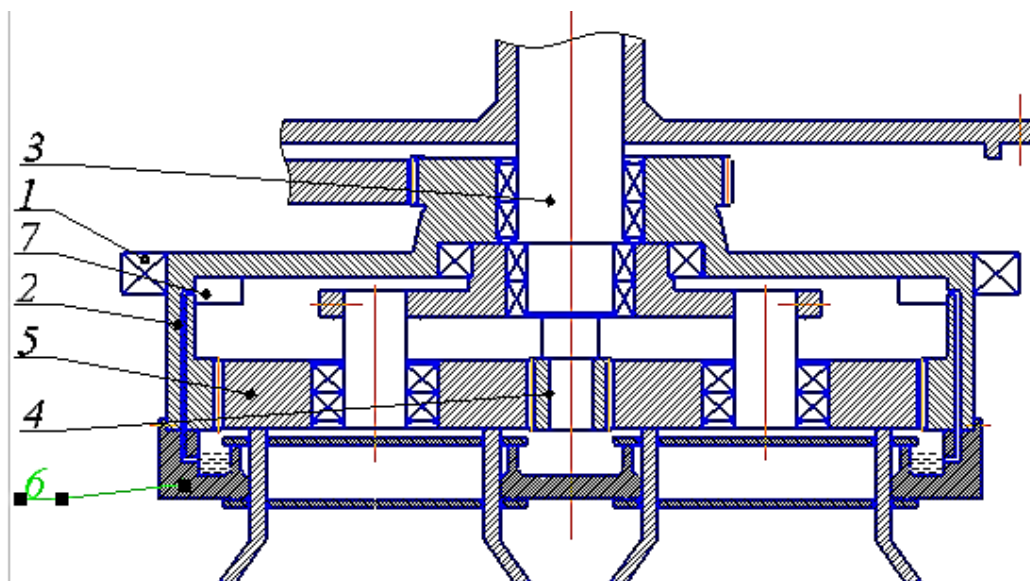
Конструктивная проработка: 1 – подшипник; 2 – корончатое колесо; 3 – вал; 4 – неподвижная шестерня; 5 – сателлит; 6 – крышка; 7 – насос
